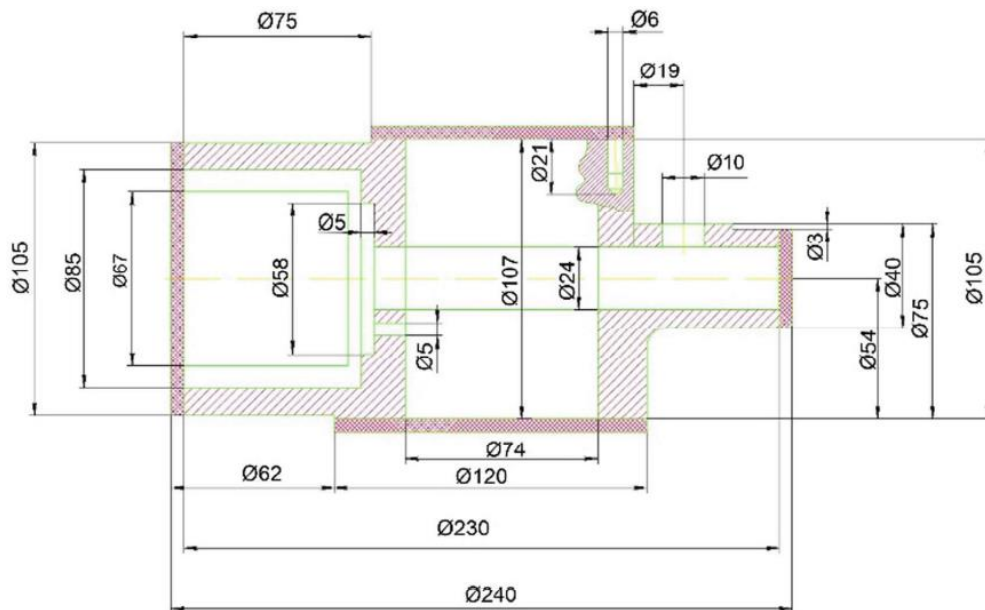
Загальний вид 2d креслення корпус деталі типу Т-207
